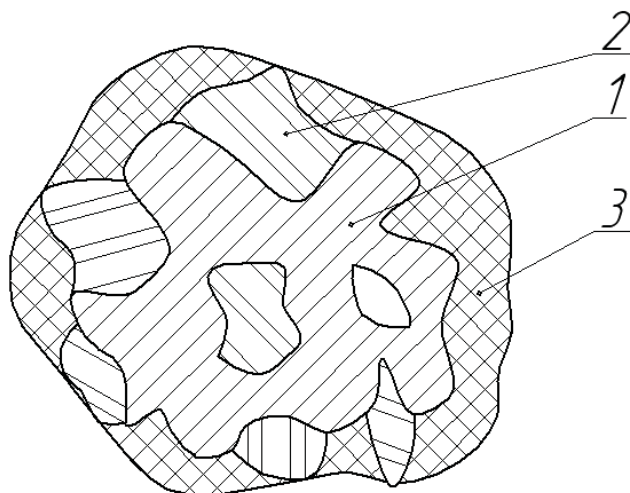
Режущий элемент устройства для магнитно-абразивной обработки
